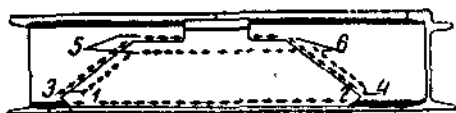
Порядок сварки вершинных стыков Индианополис.
